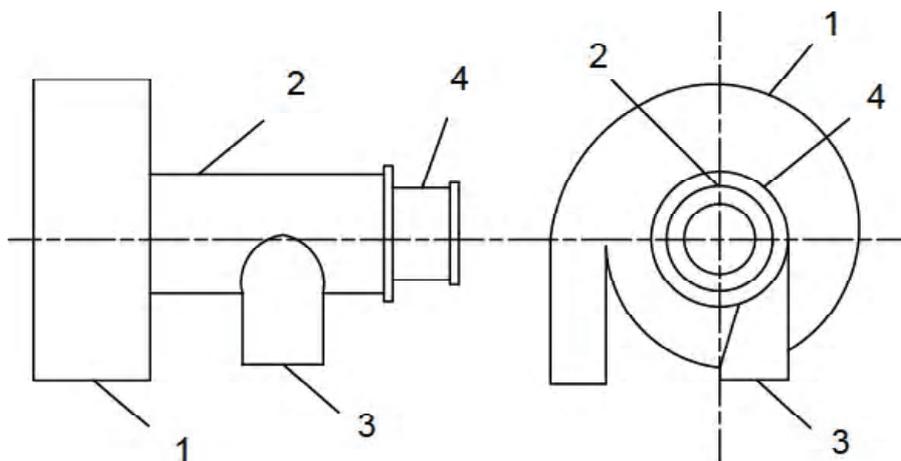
Схема пылеконцентратора: 1 – улиточный закручиватель; 2 – сепарационная камера; 3 – тангенциальный патрубок; 4 – аксиальный патрубок.
